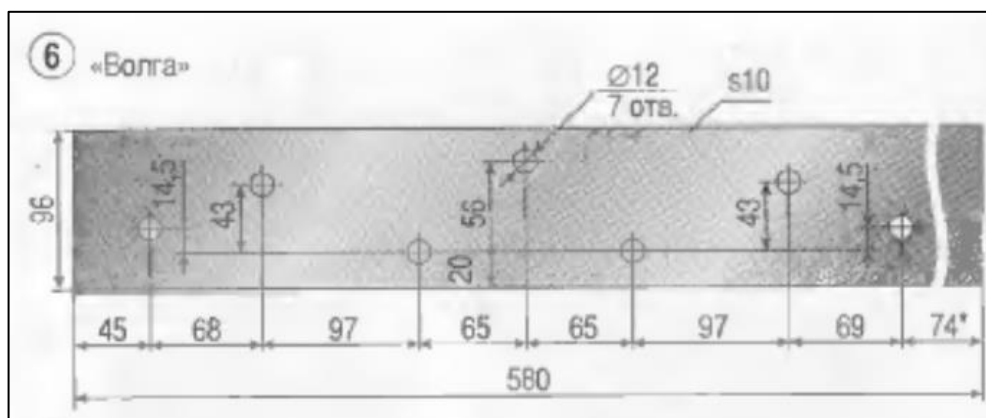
Разметка отверстий и пазов в несущей пластины для автомобиля «Волга»
